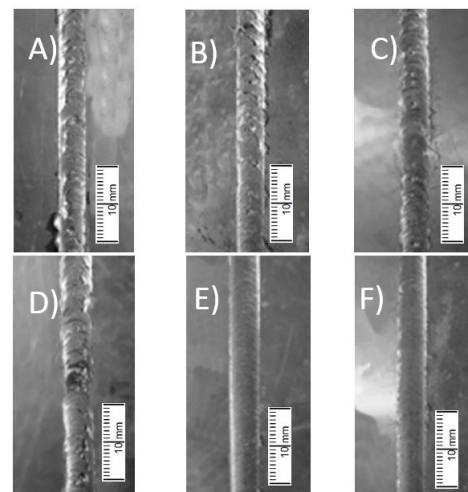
Aspectos superficiales de la soldadura para las diferentes velocidades de rotación de la herramienta.
